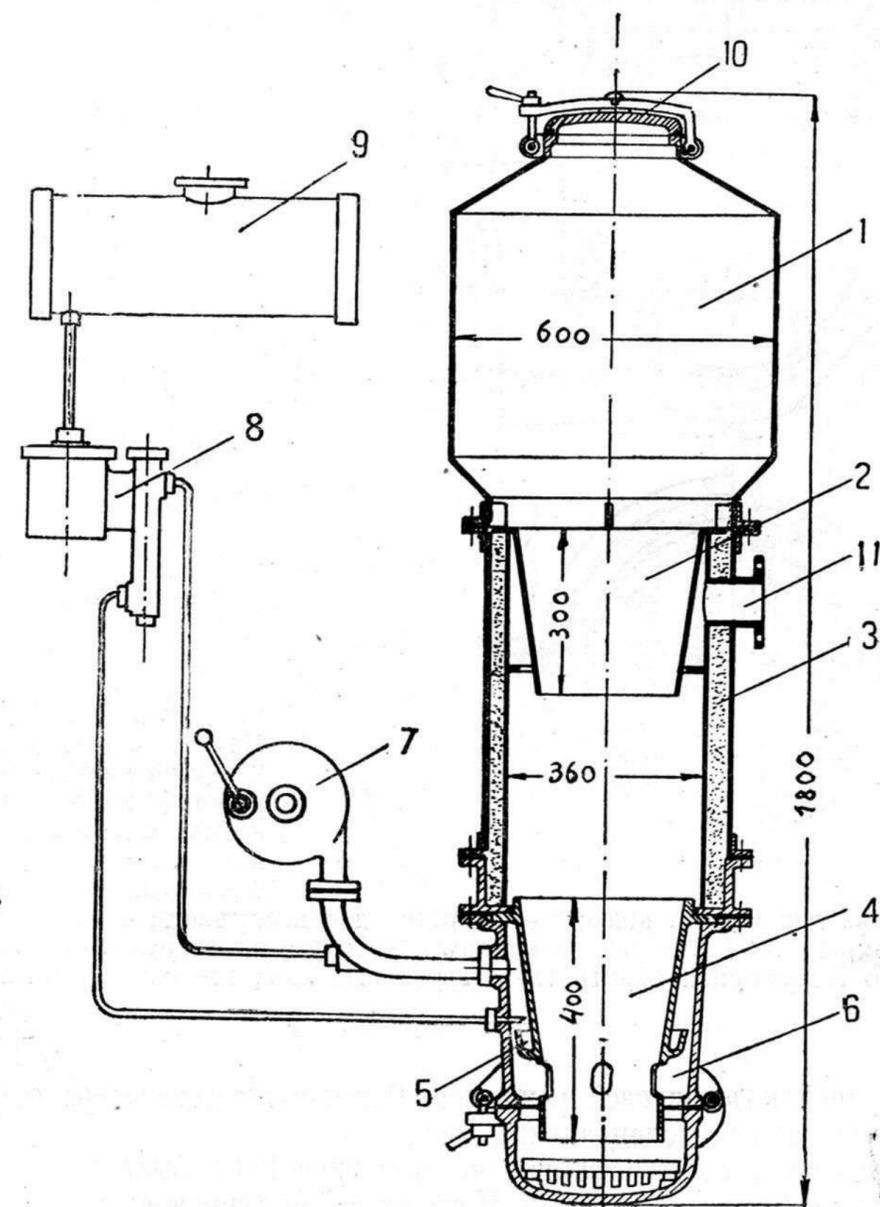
Газогенератор Тип. 1—бункер; 2—загрузочный конус; 3—асбесто-шамотная обкладка шахты; 4—топливник; 5—мгновенный испаритель; 6—подвод воздуха; 7—вентилятор для розжига; 8—автоматический регулятор; 9—водяной бачок; 10—загрузочный люк; 11—патрубок для отсоса газа
